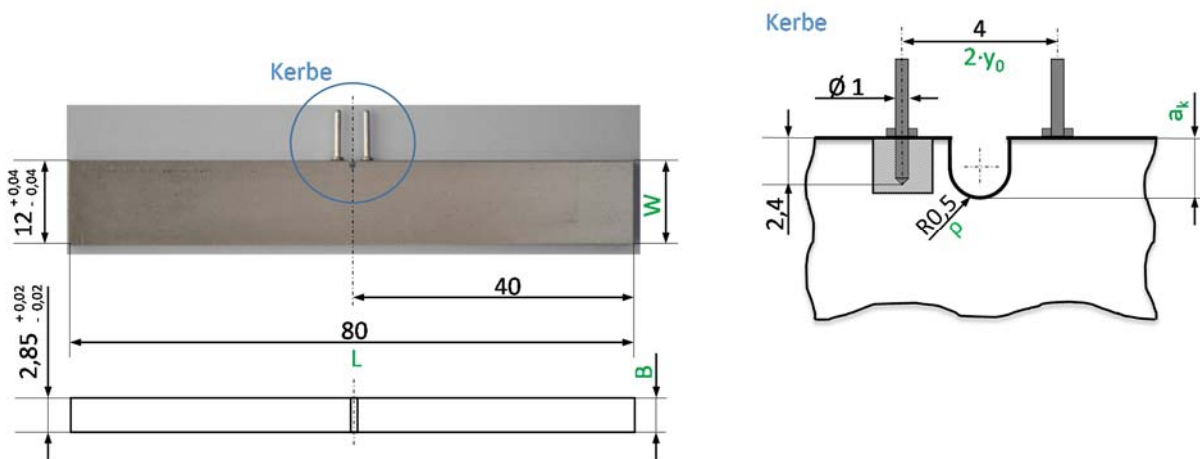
SEN-Probengeometrie (Bemaßung in mm)
